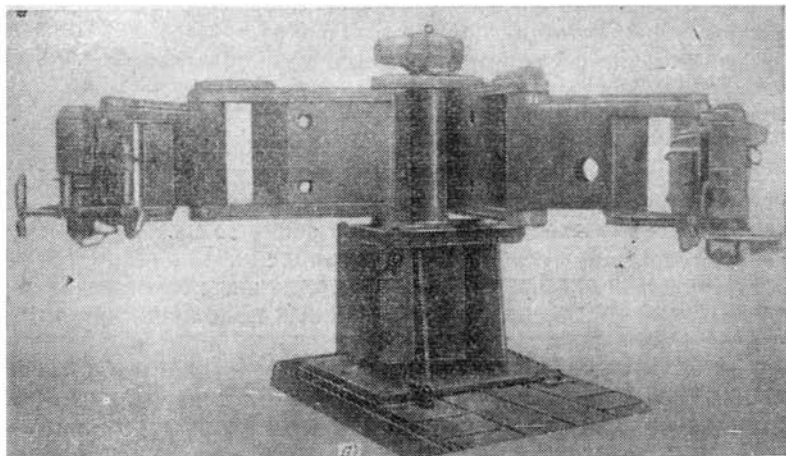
Радиально-сверльно-фрезерный станок ОС-86:
